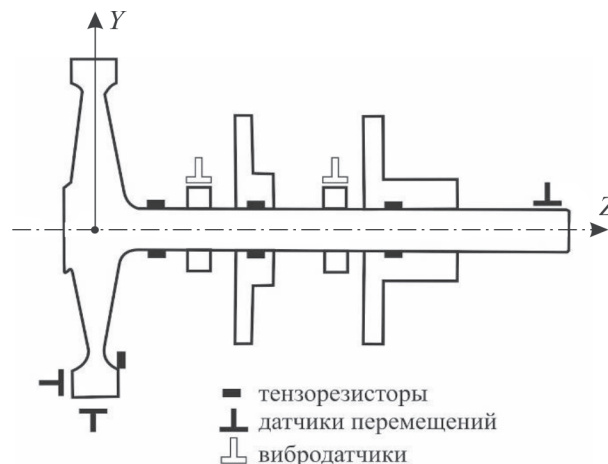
Схема установки тензорезисторов и датчиков на вал ротора ТНА-150
